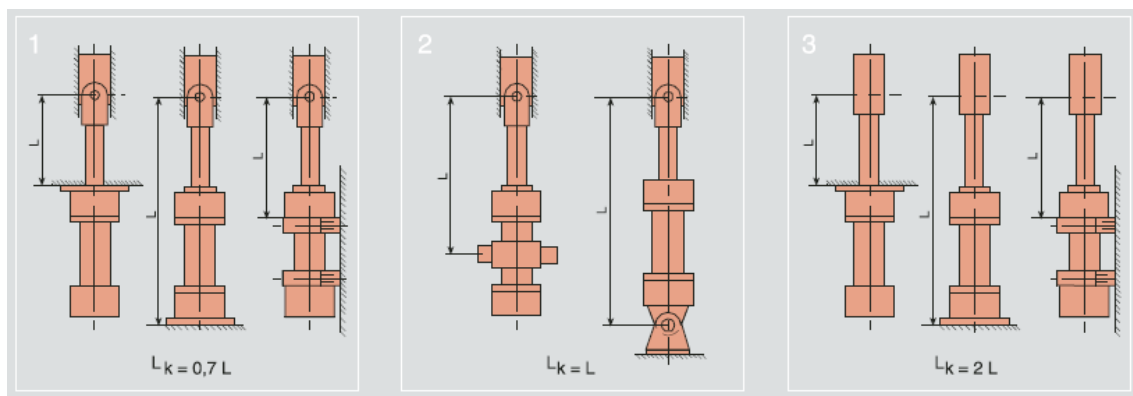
Tipos de fijación de los cilindros principal y secundario
